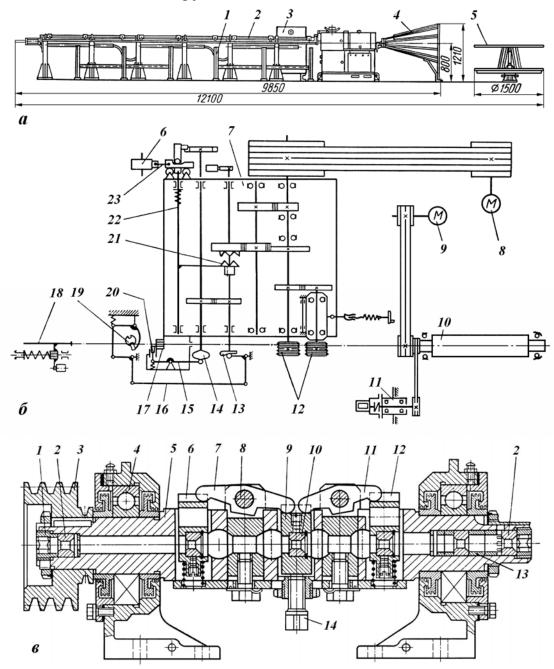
Правильно-отрезной станок СМЖ-357: a – общий вид станка; 6 – кинематическая схема; e – правильный барабан
